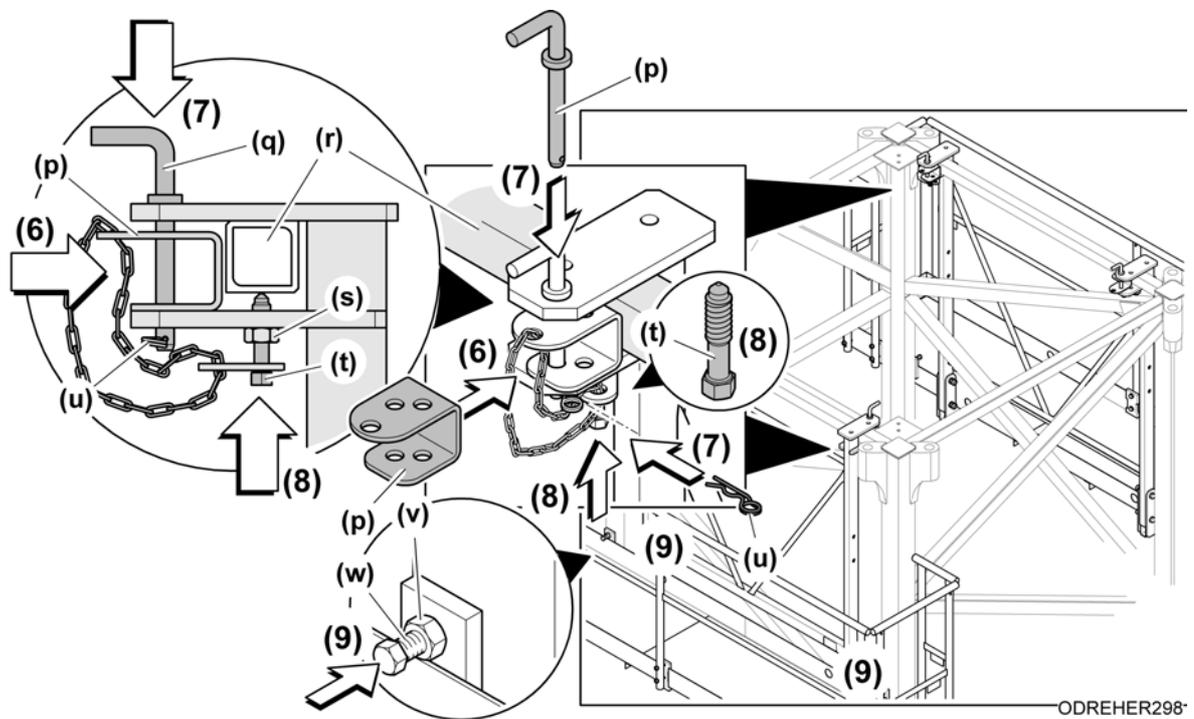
Montagepodest verspannen (Beispiel: vormontiert für EC-B Kran)
